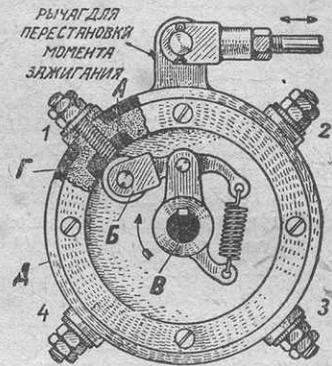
Роликовый замыкатель батарейного зажигания четырехцилиндрового двигателя.
